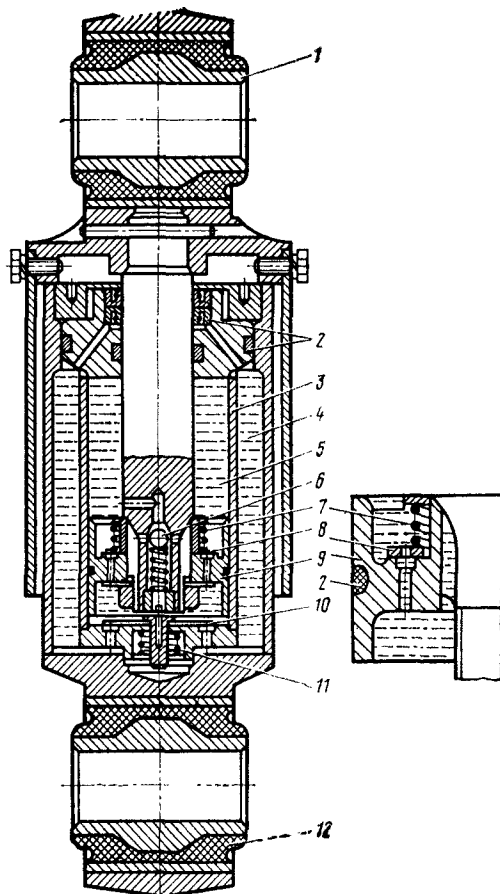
Гидравлический гаситель колебаний: 1, 12 — резиновые втулки; 2 — уплотнения; 3 — цилиндр рабочий; 4 — масляный резервуар; 5 — полость рабочего цилиндра; 6 — шариковый предохранительный клапан; 7, 11 — пружины; 8, 10 — клапаны; 9 — поршень
